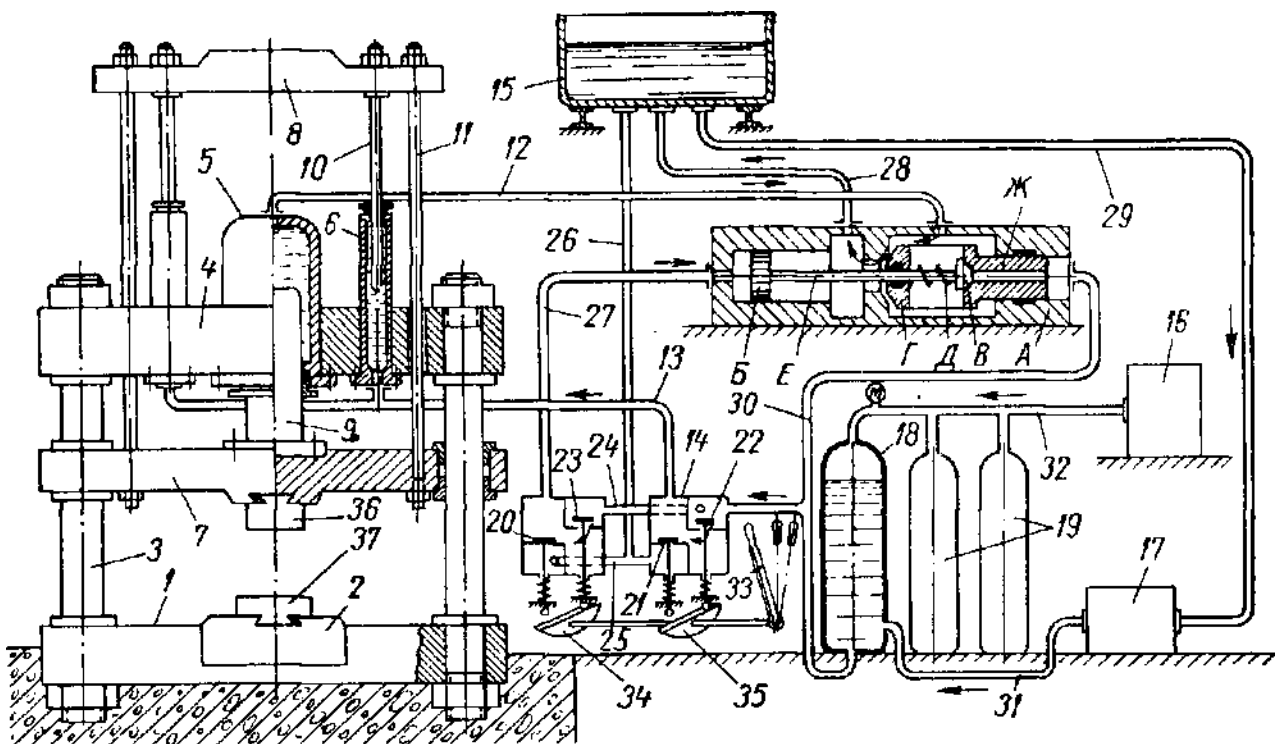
Принципова схема пристрою гідравлічного преса
